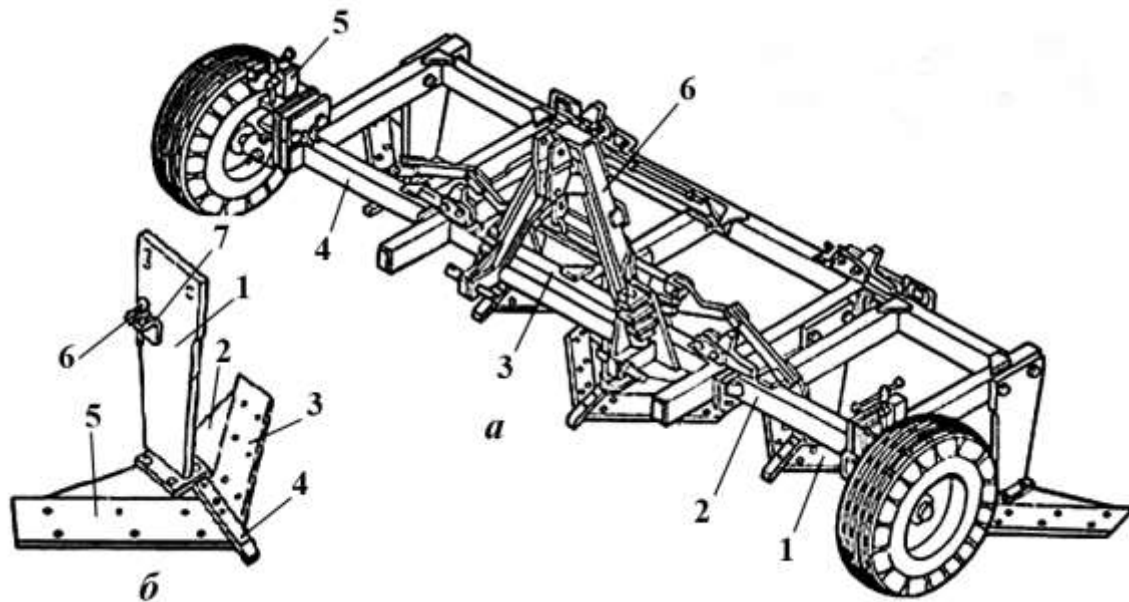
Плоскоріз-глибокорозпушувач ПГ-3-5:
